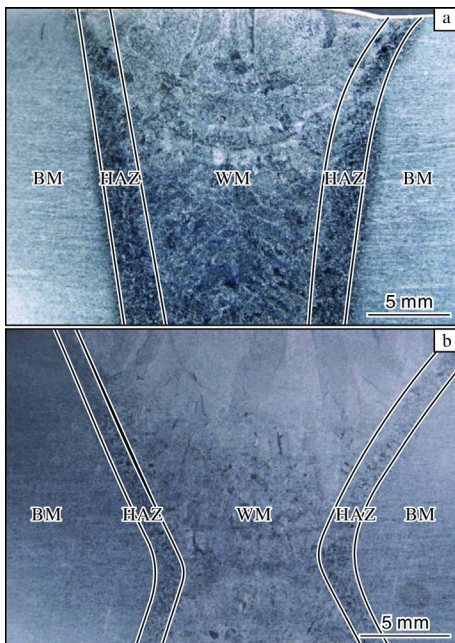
TA5 钛合金焊接接头宏观形貌
